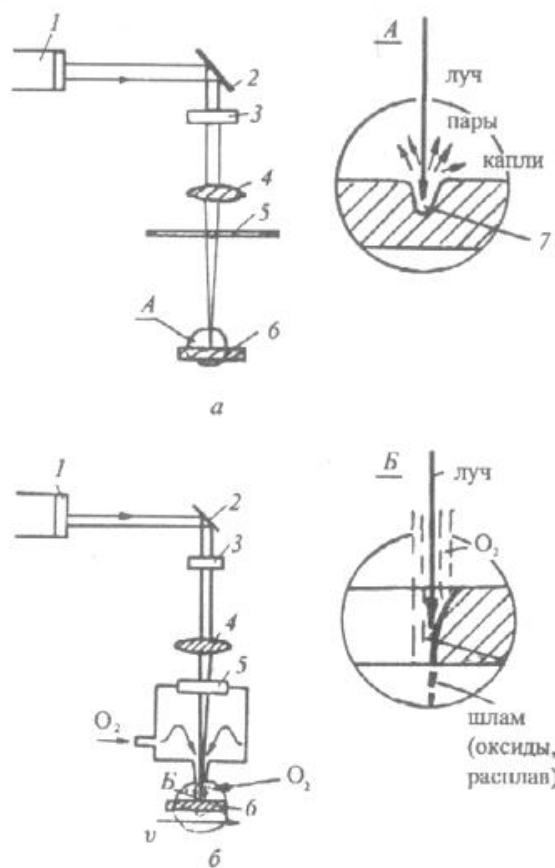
Условные схемы лазерной обработки (а) и газолазерной резки (б):
